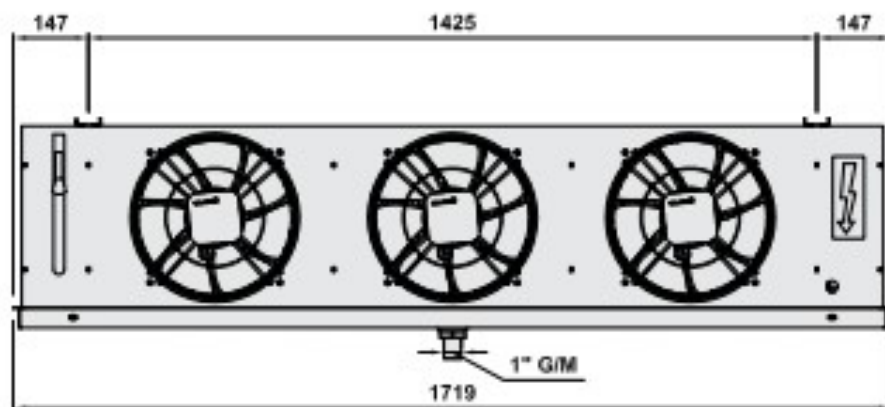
Габаритные размеры воздухоохлаждителя «КСЕН 303 S3»
